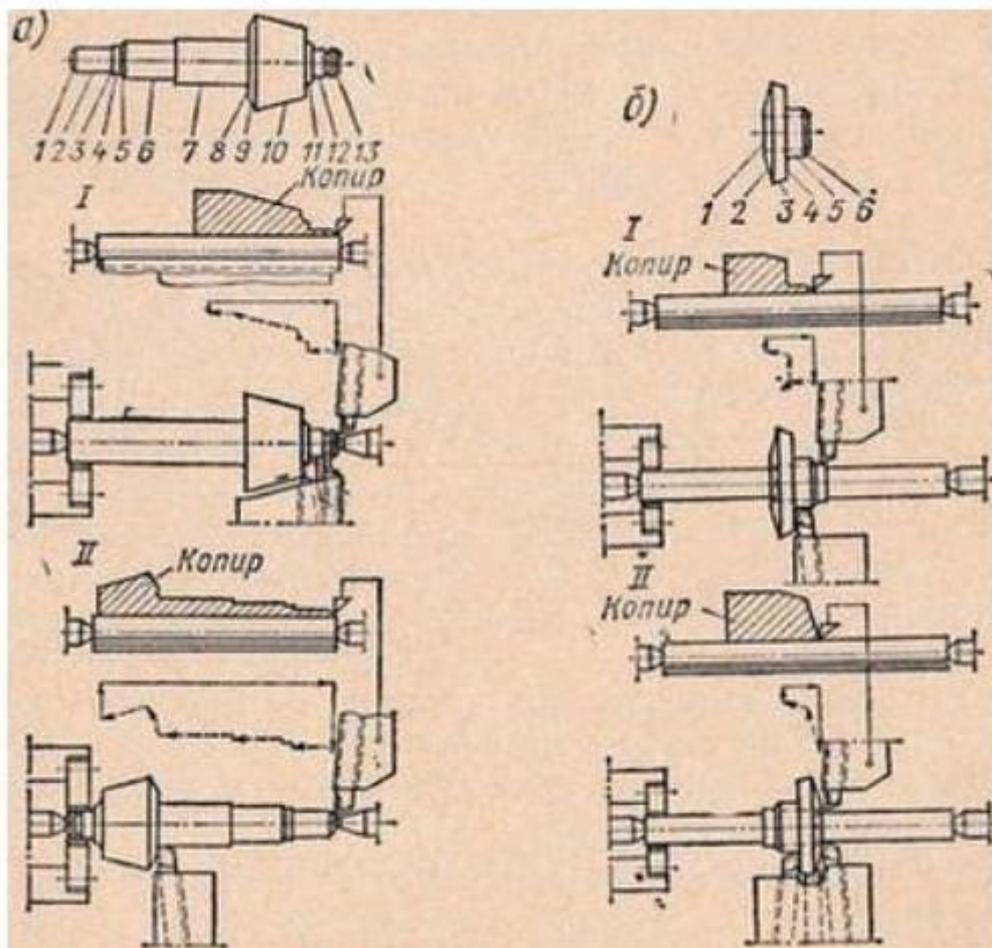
Схеми наладки обробки заготовок конічних зубчастих коліс класу «вал» (а) і класу «втулка» (б)
